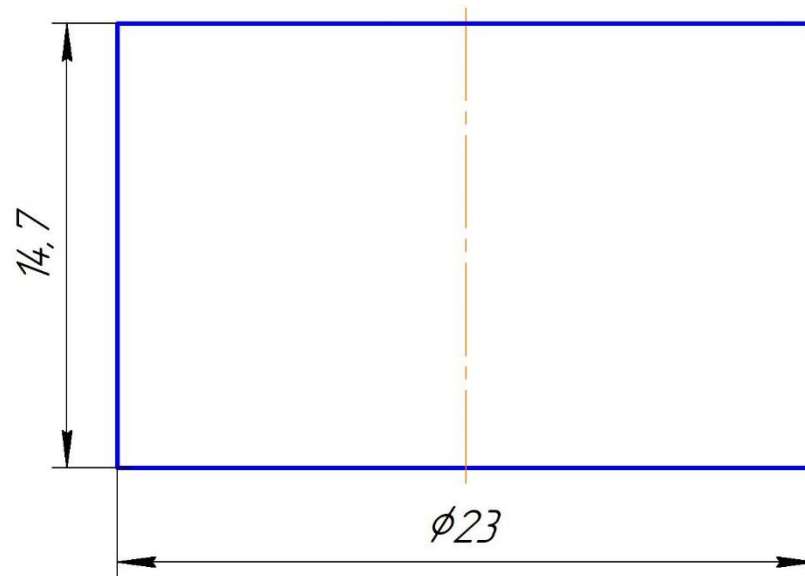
Ескіз заготовки для напівфабрикату деталі «Втулка».
